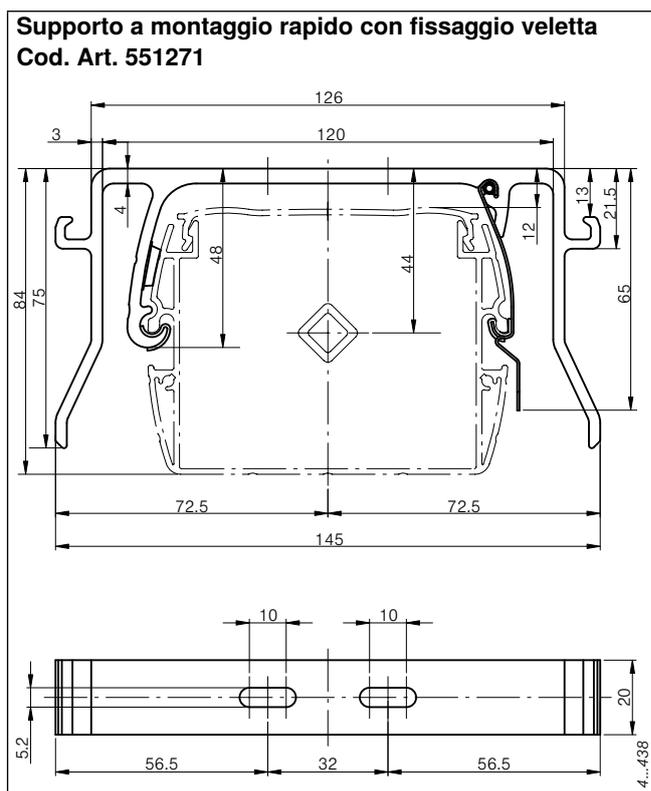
Supporto a montaggio rapido con fissaggio veletta
